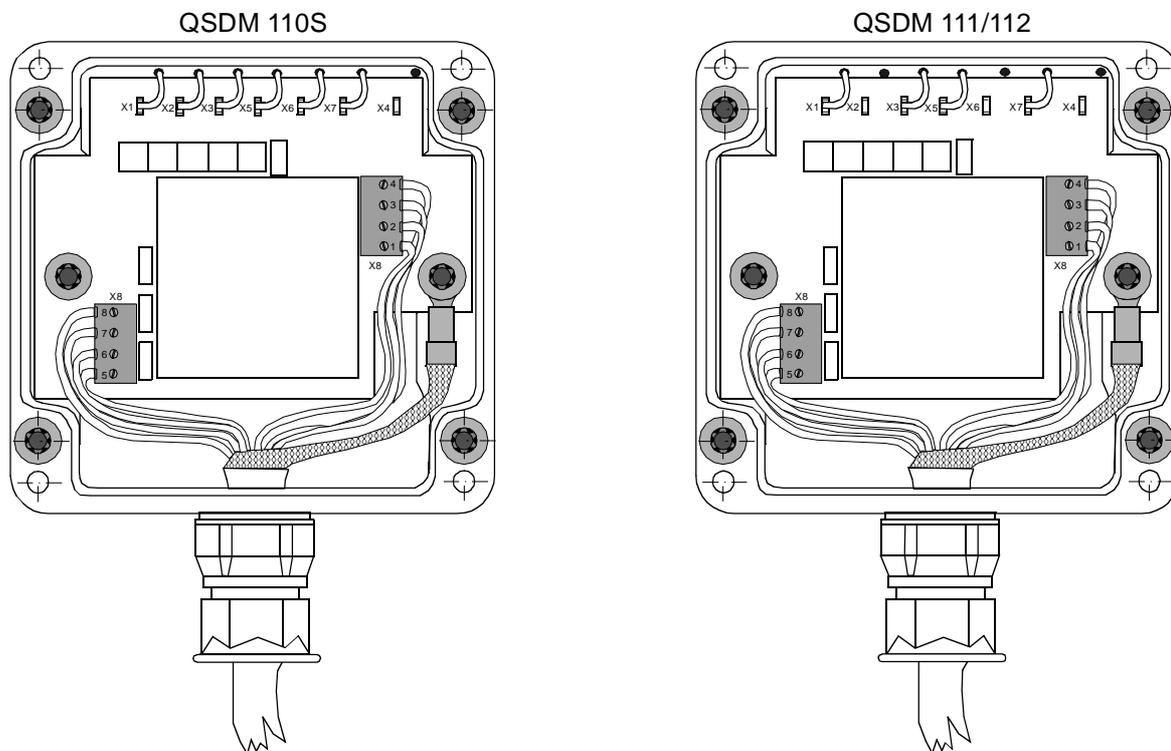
Amplificador de sinal QSDM 111R montada na bobina sensora QSDM 110S
